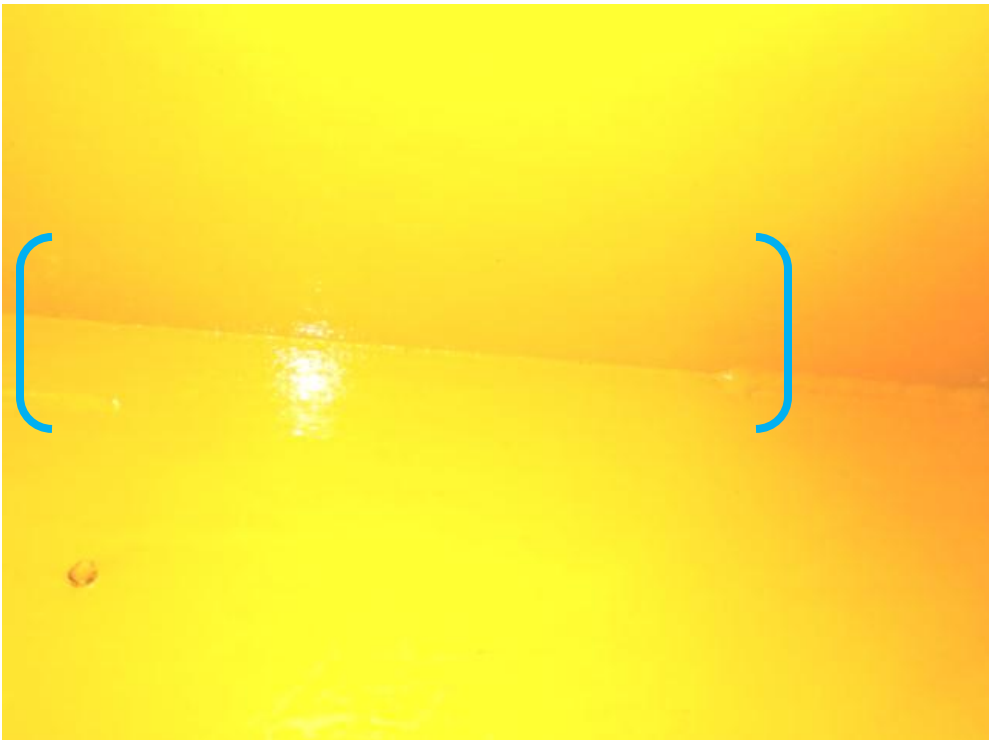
FALTA DE CORDÓN DE SOLDADURA
